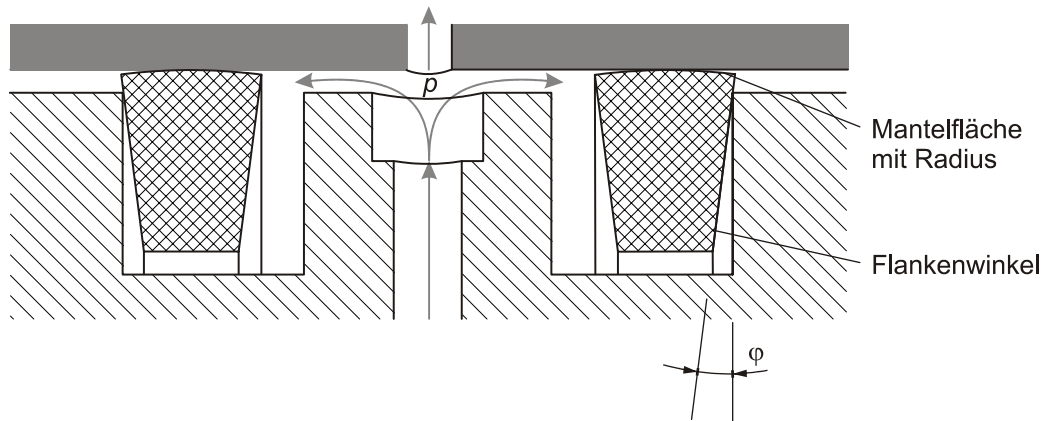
Dichtringe mit schräger Flanke und verrundeter Mantelfläche [21]
